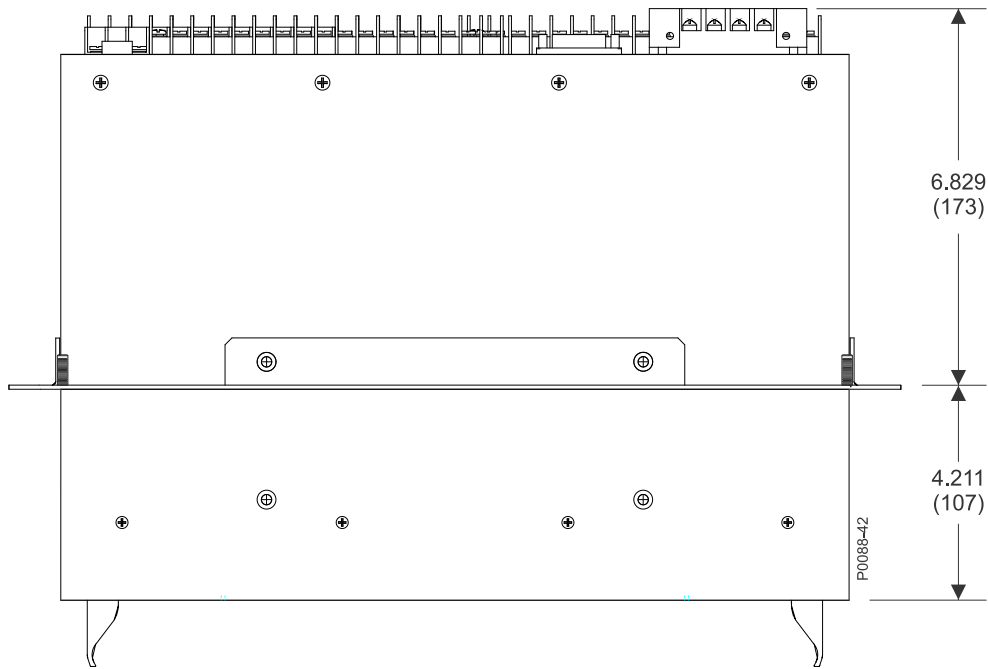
Vista superior del DECS-400 con la placa protectora instalada
